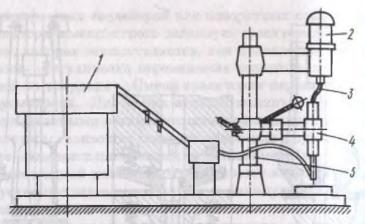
Компоновка механизмов на рабочем месте сборщика
